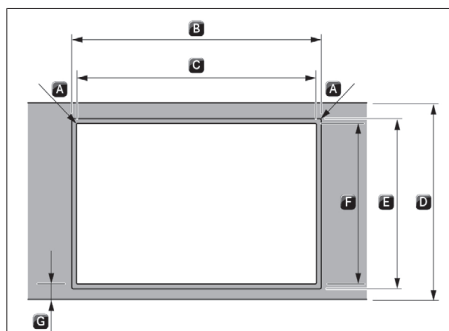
Dimensiones de recorte para instalación enrasada
